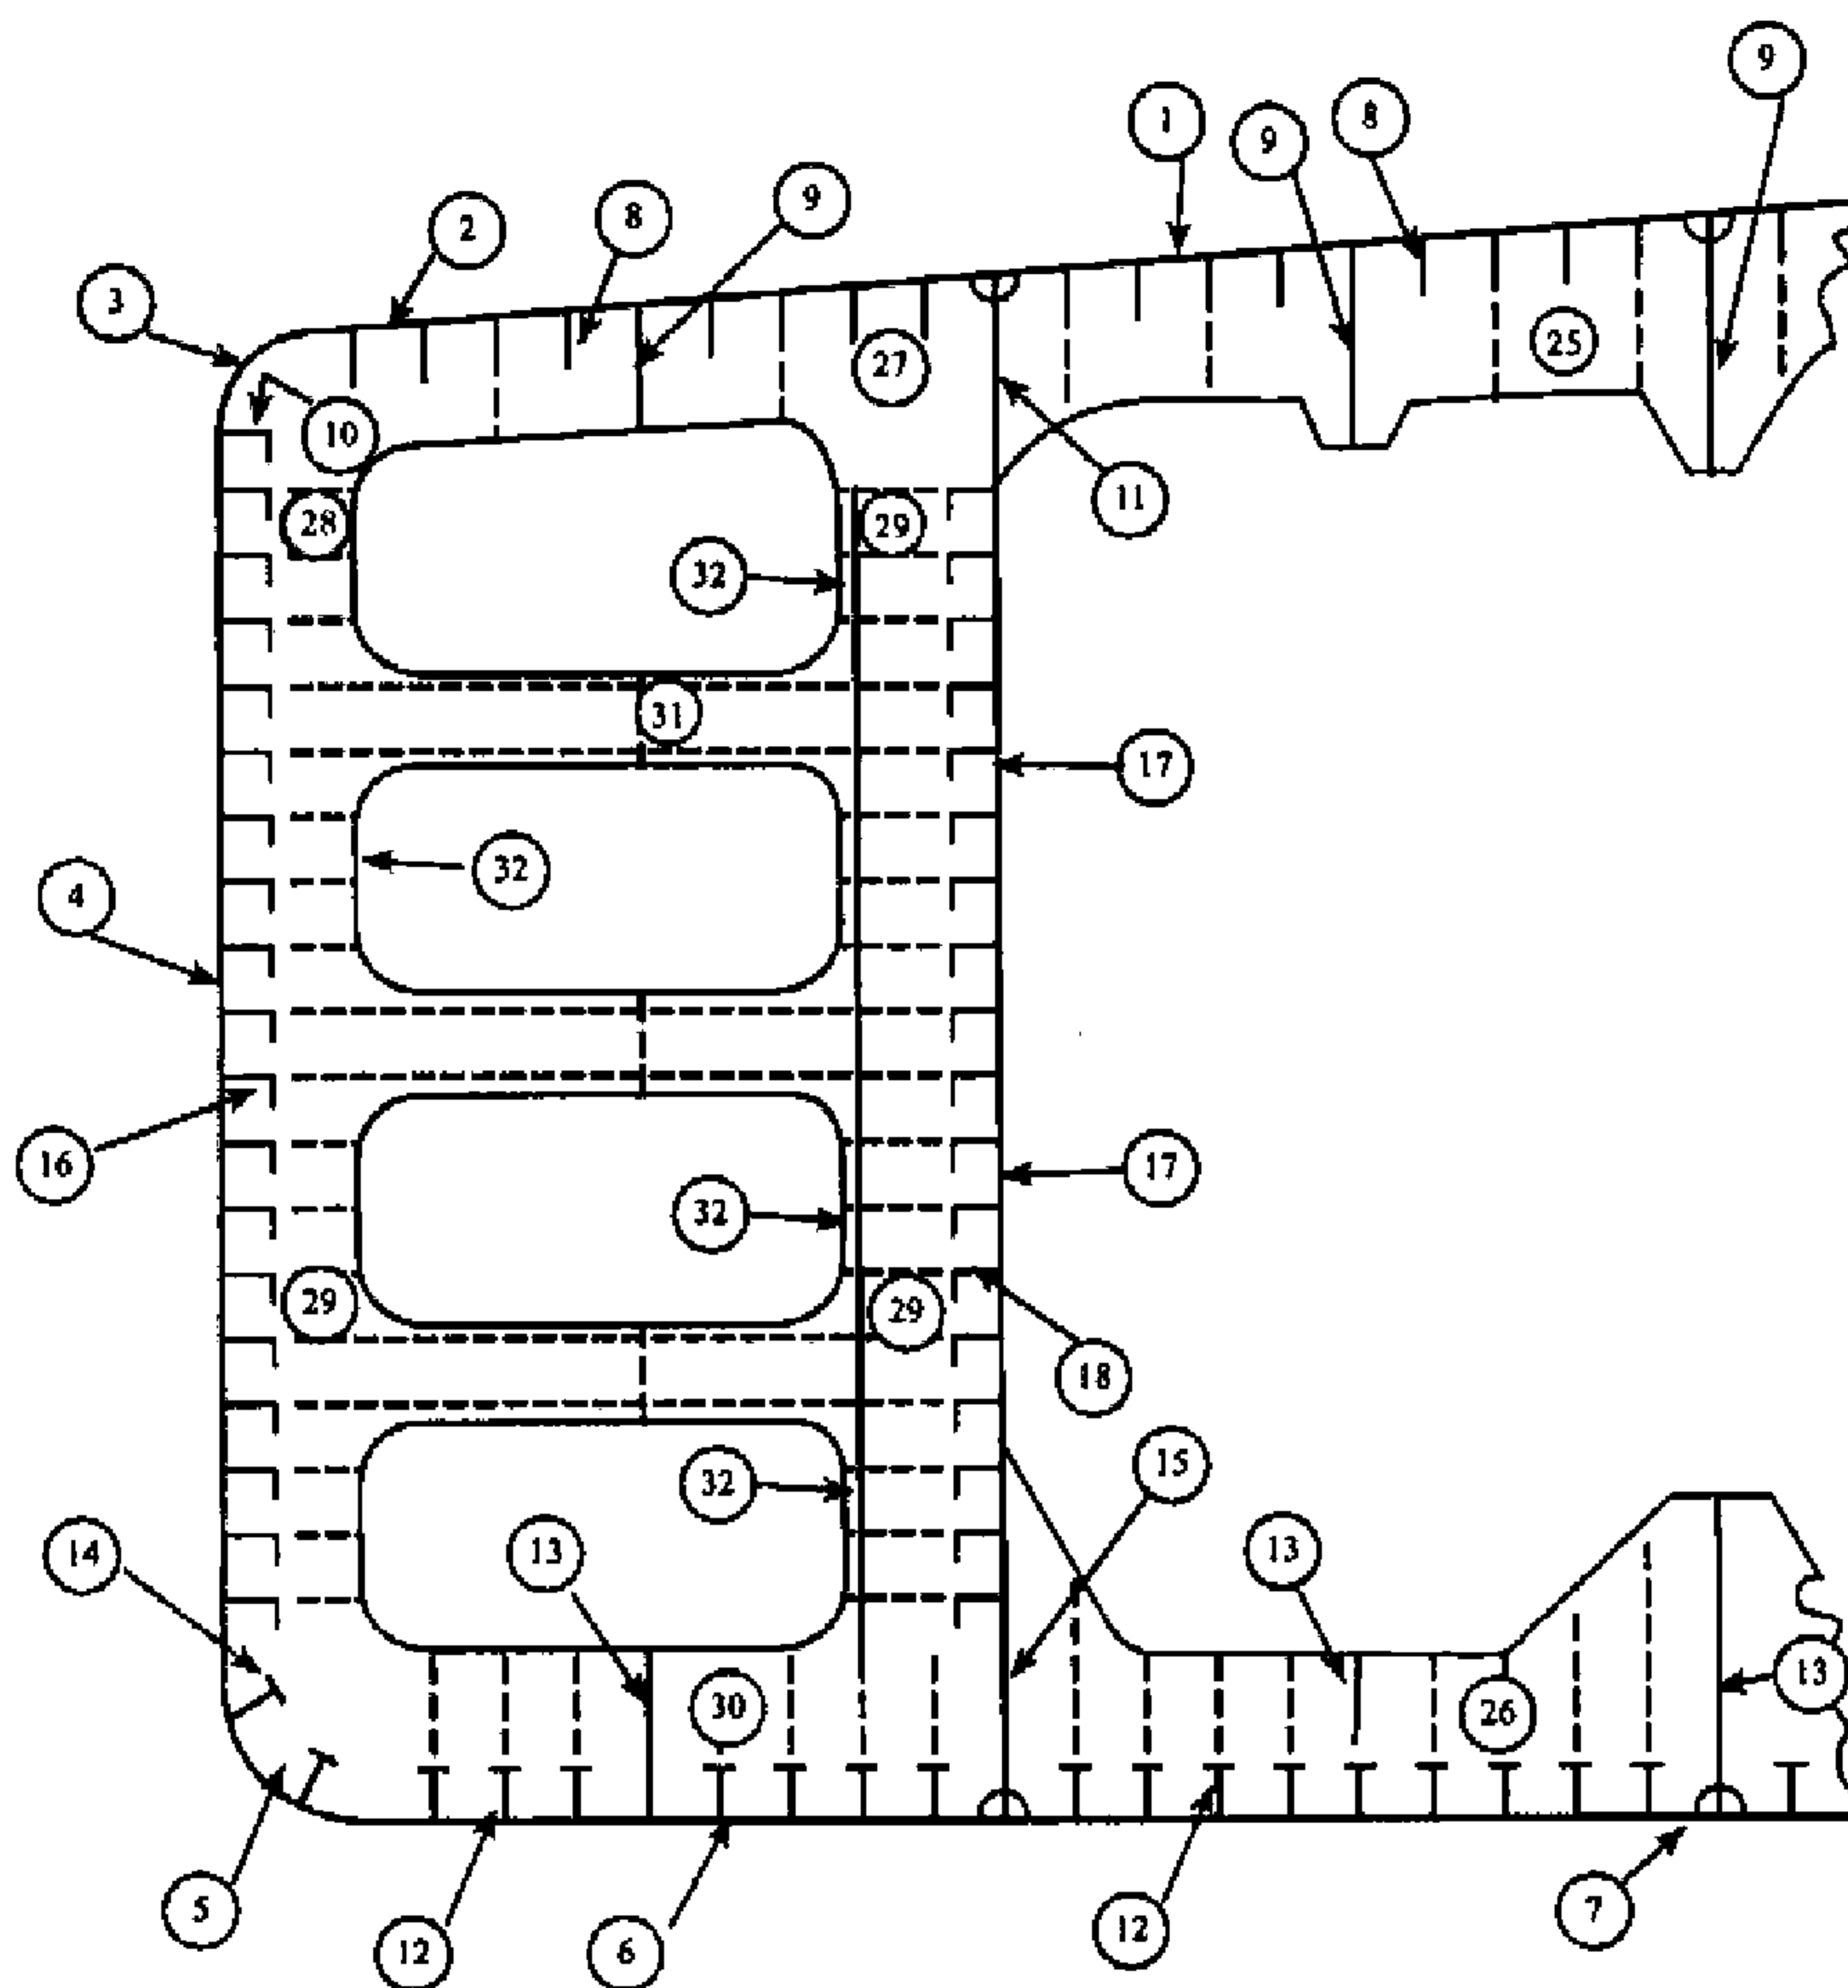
Типичное сечение корпуса танкера с обозначением элементов корпусных конструкций:
